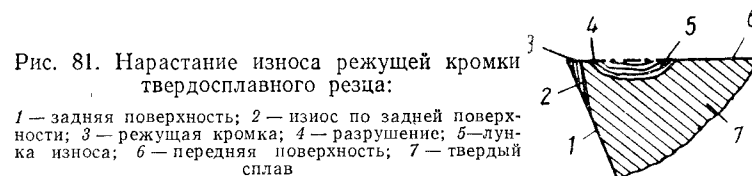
Нарастание износа режущей кромки твердосплавного резца:
